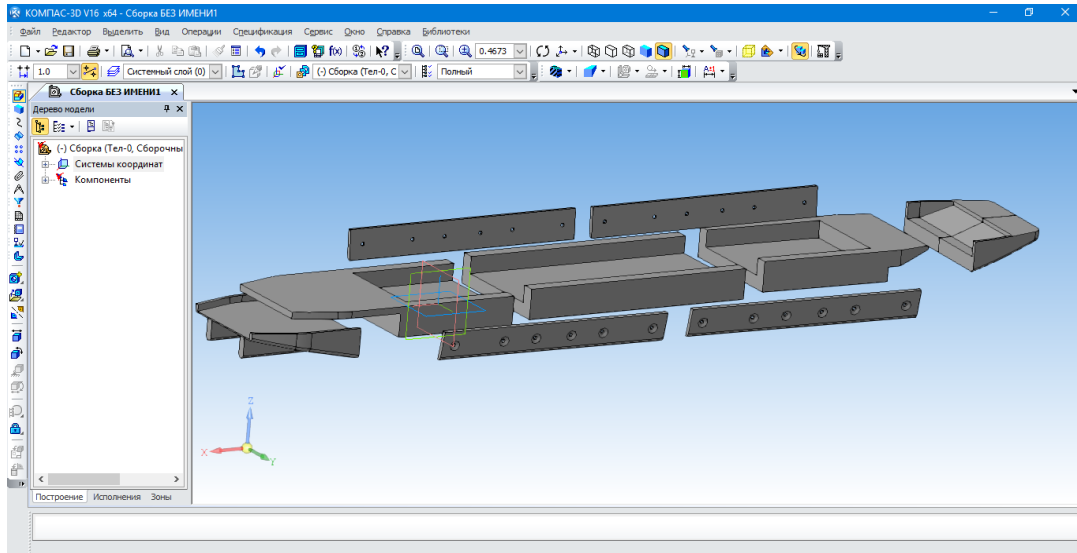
Процесс сборки основных элементов, носовой и кормовой частей 3D-модели НС
